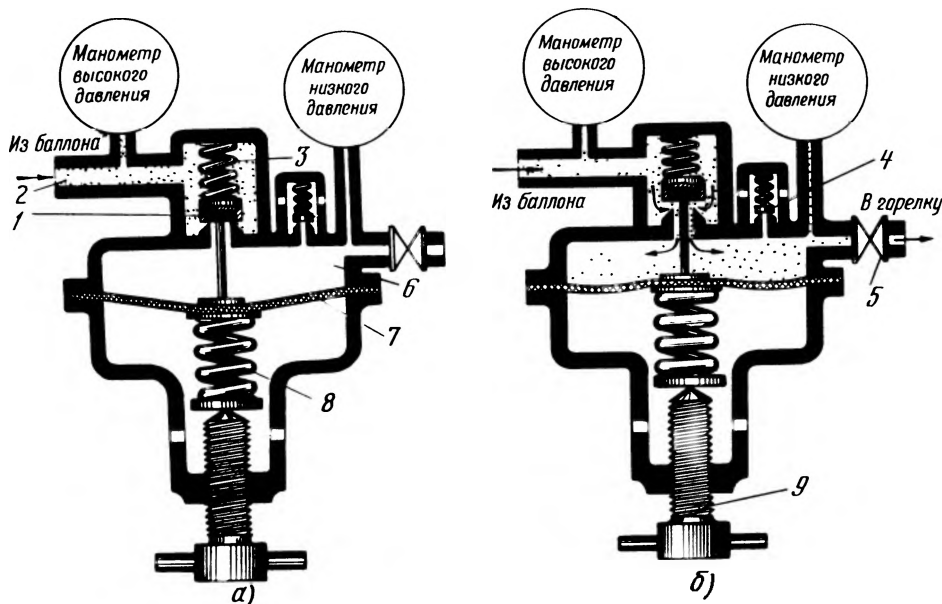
Схема устройства и работы редуктора: а — нерабочее, б — рабочее положения
